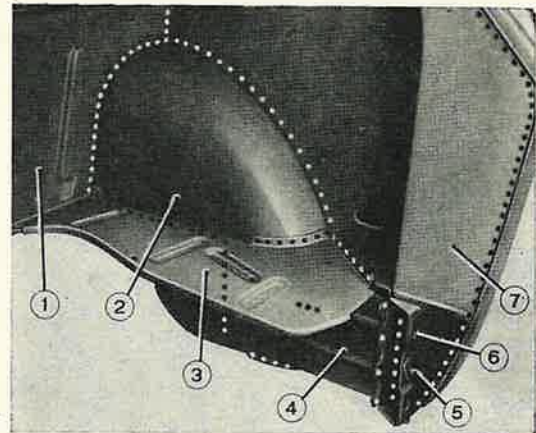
Indication des liaisons par points de soudure, des tôles de protection du compartiment moteur et du passage de roue arrière droit.
